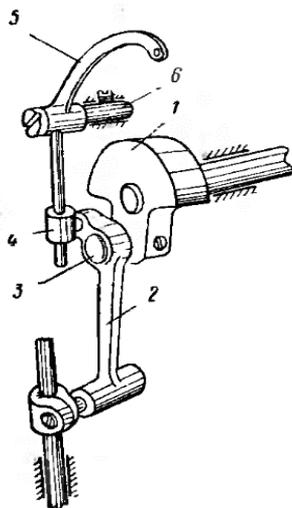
Кулисно-рычажный механизм нитепритягивателя
